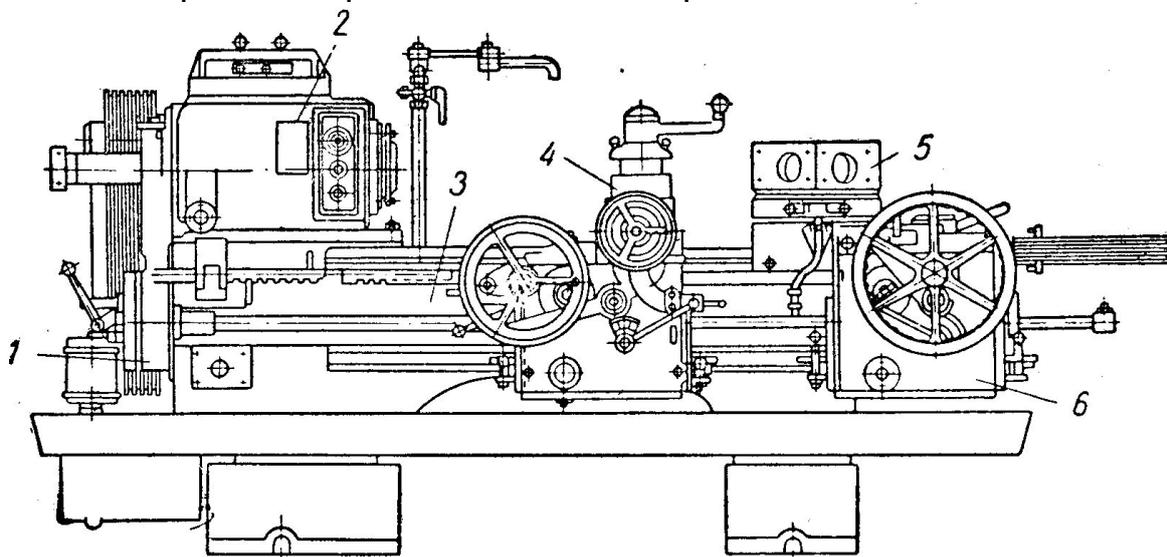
Общий вид токарно-револьверного станка: 1 – коробка подач; 2 – передняя бабка; 3 – станина; 4 – передний суппорт; 5 – револьверная головка; 6 – каретка
